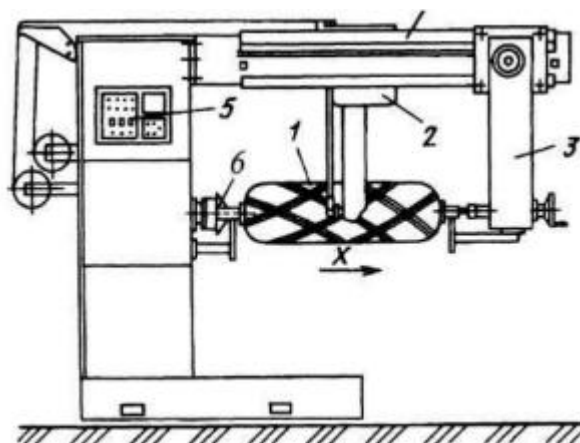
Схема пристрою намоточного верстата порталного типу
